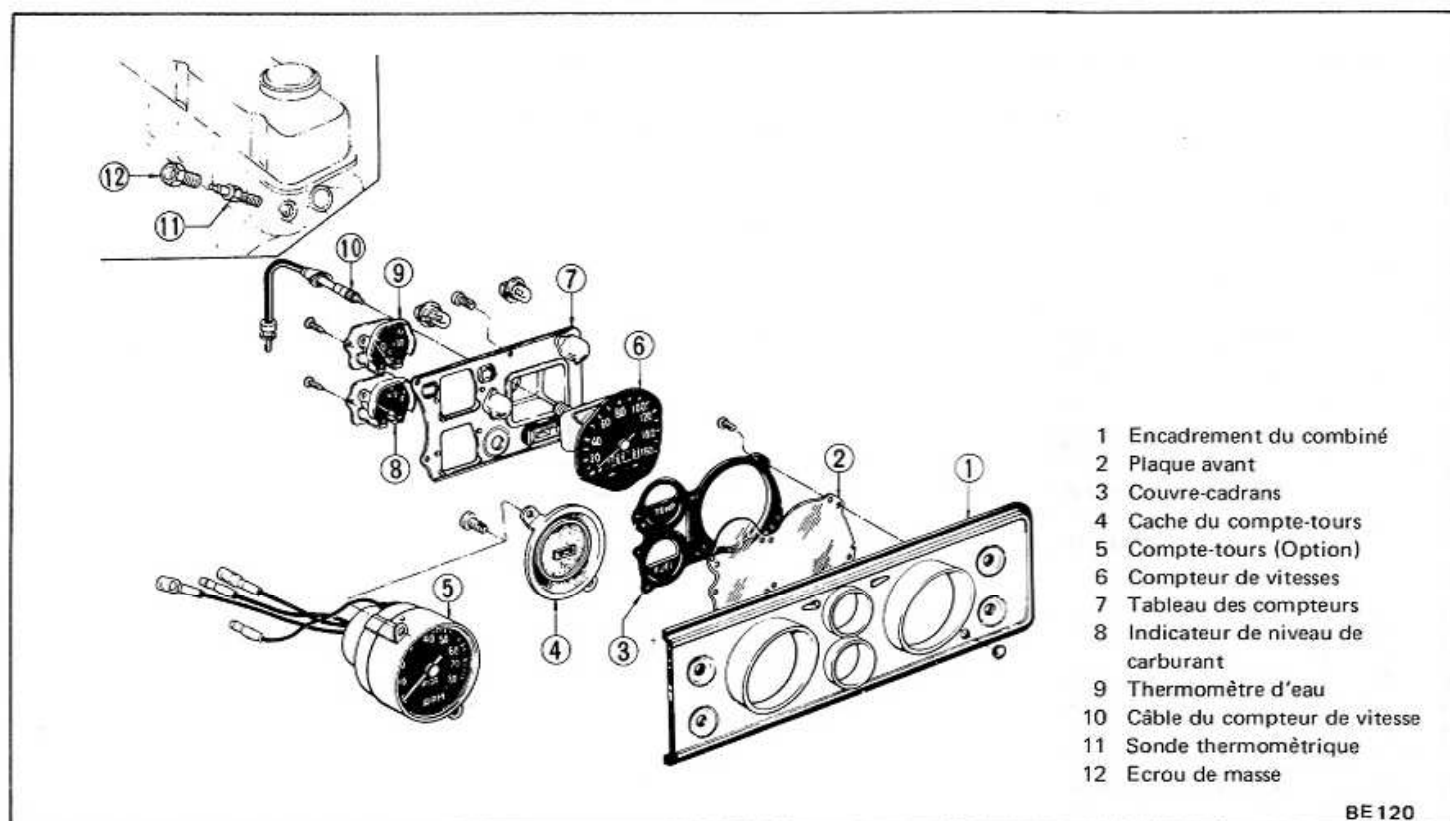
Vue éclatée des compteurs et des indicateurs
